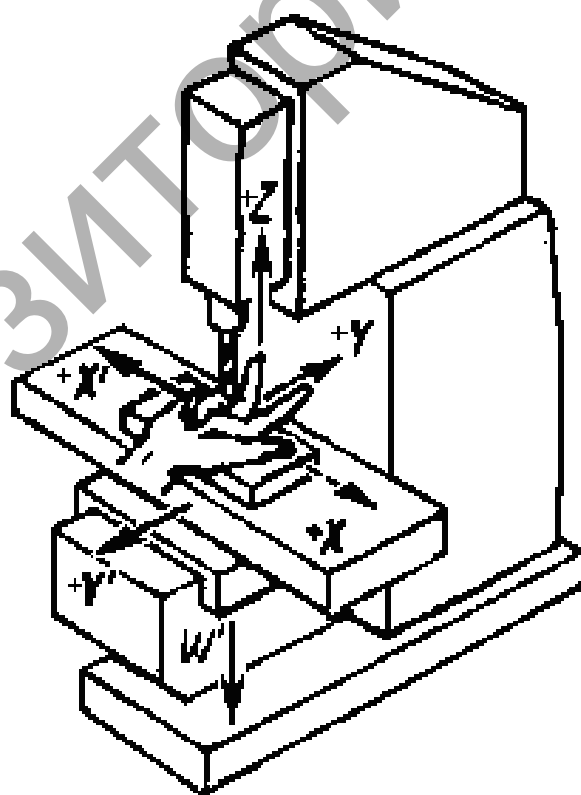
Обозначение координат для фрезерных станков с ЧПУ
